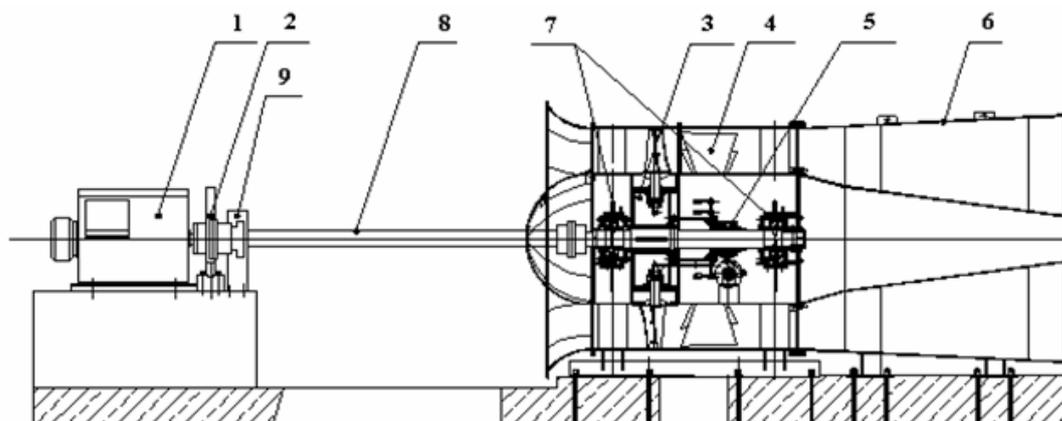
Реверсивный вентиляторный агрегат ВО-36К со сменными и поворотными на ходу лопатками рабочего колеса: 1 – электродвигатель (2000 кВт, 600 об/мин); 2 – электромеханический тормоз; 3 – рабочее колесо с поворотными на ходу сдвоенными листовыми лопатками; 4 – неповоротные лопатки спрямляющего аппарата; 5 – механизм одновременного поворота лопаток рабочего колеса; 6 – диффузор; 7 – подшипниковые опоры; 8 – трансмиссионный вал; 9 – датчик оборотов
